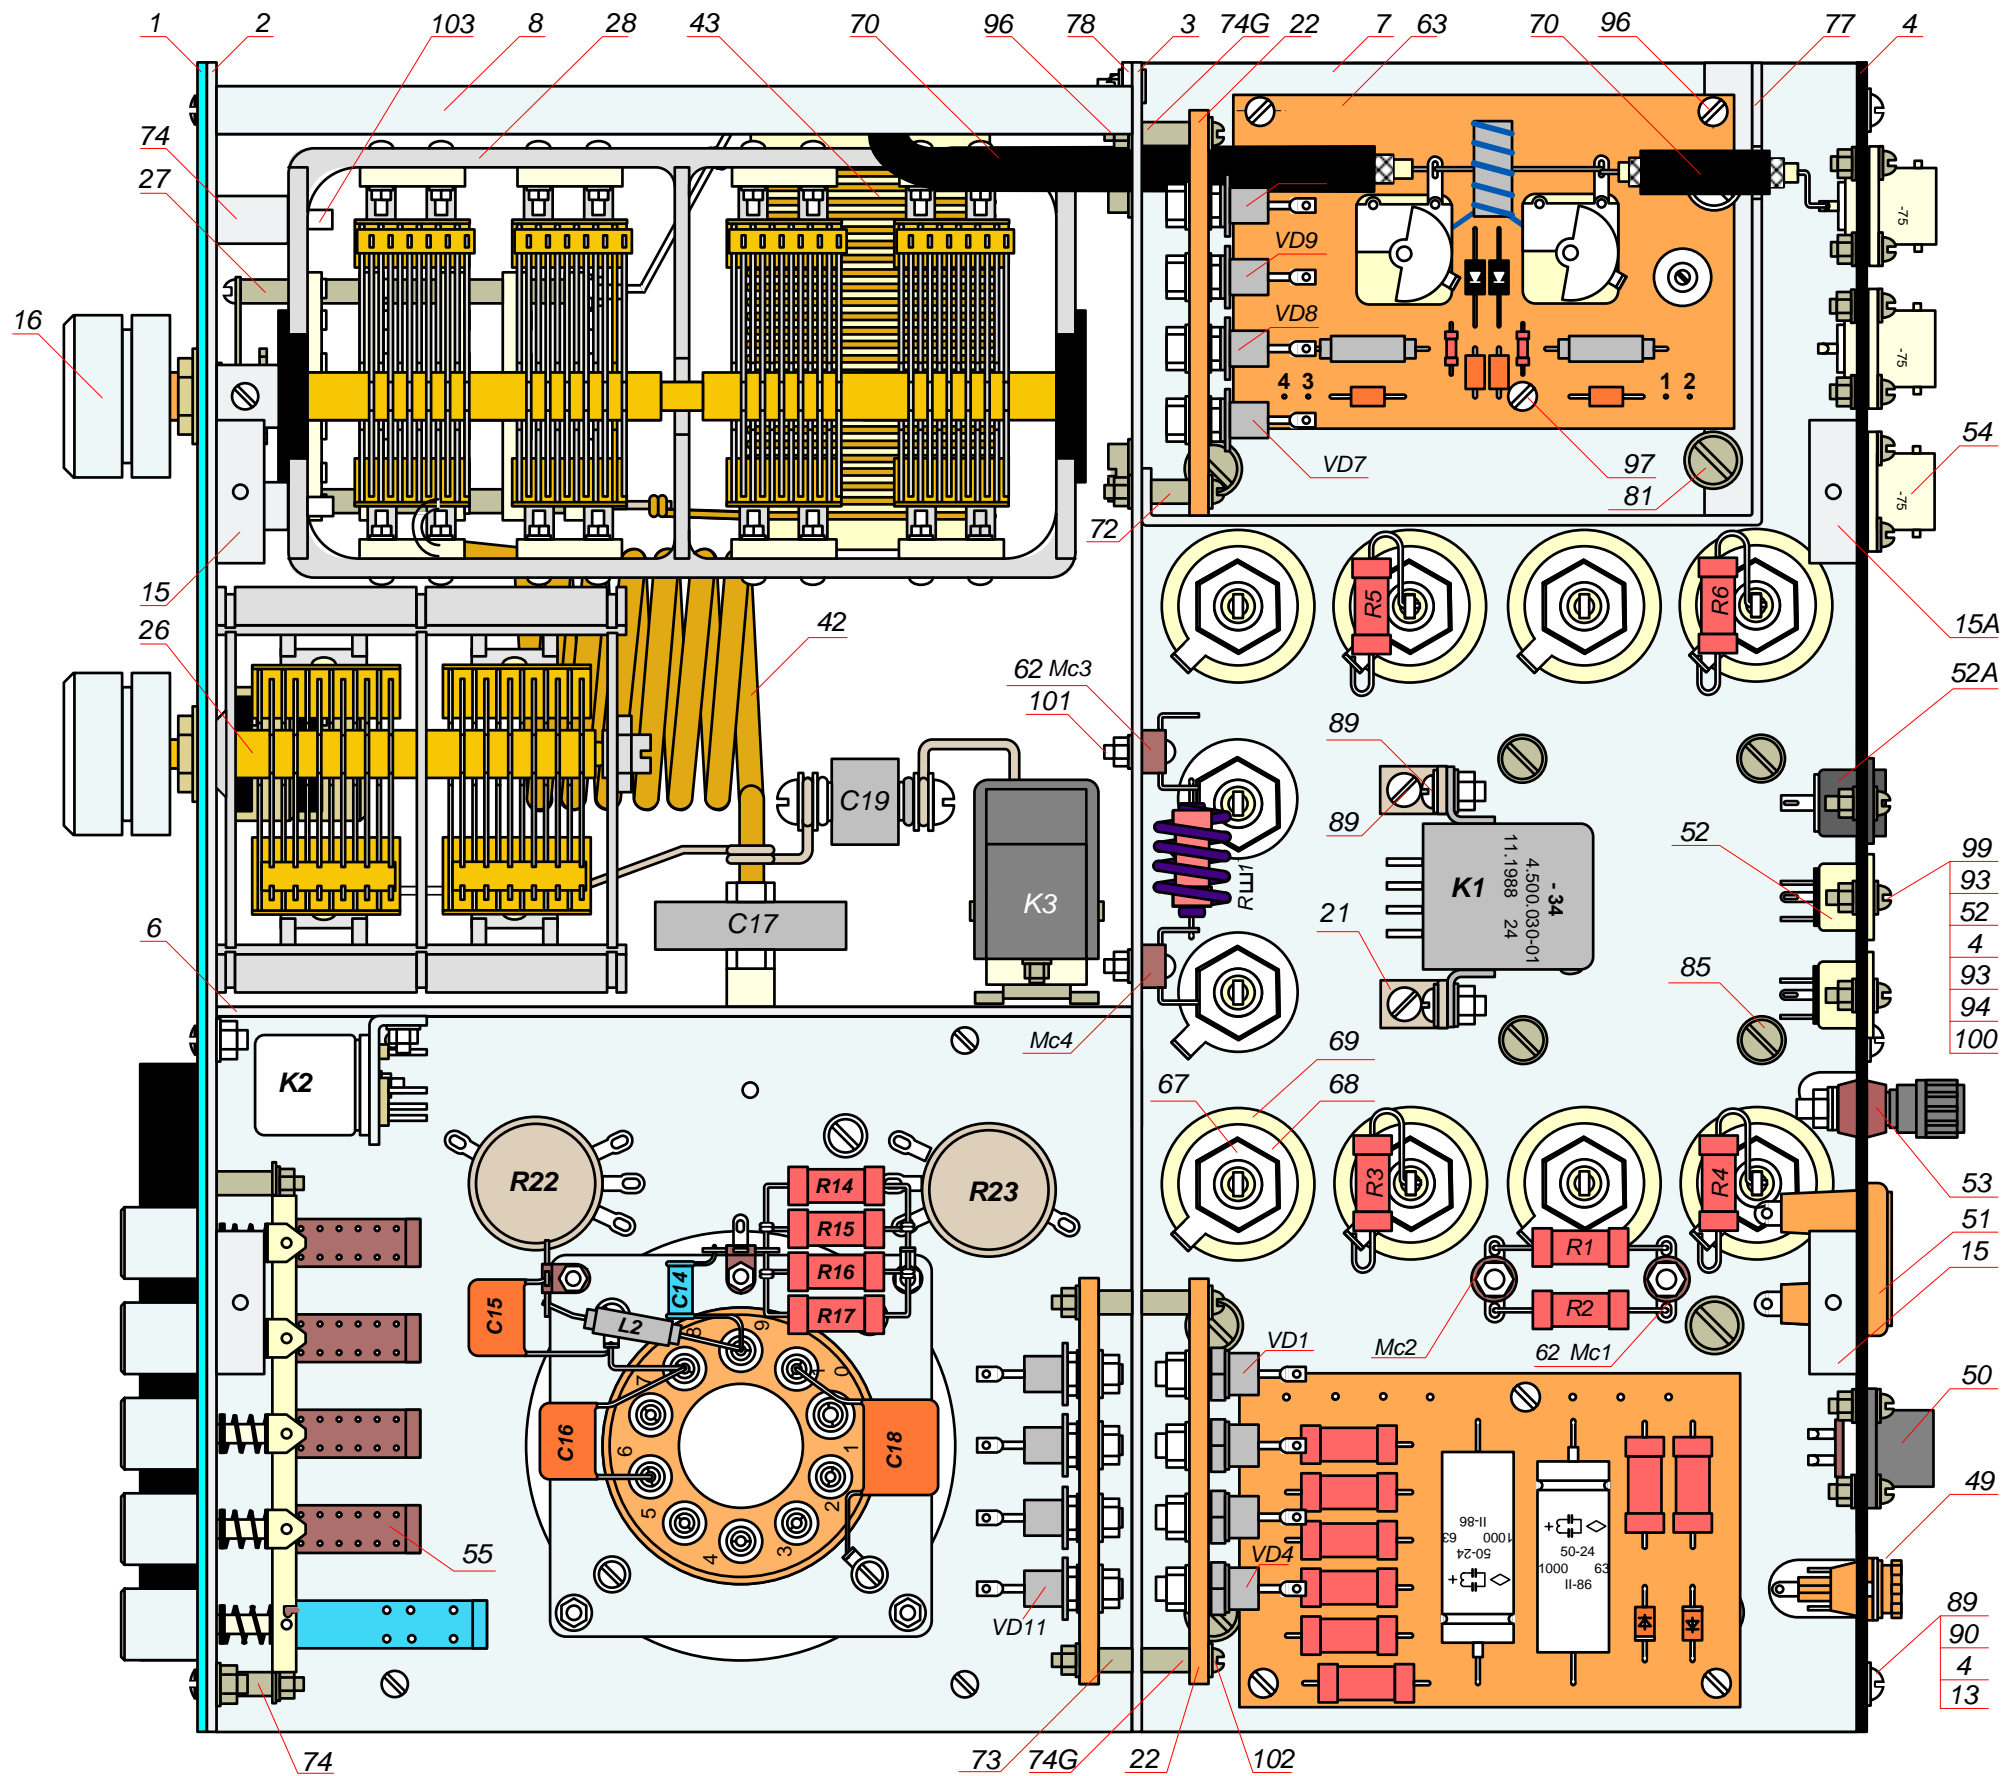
А. Сборочный чертёж усилителя DVA-300А. Вид сверху со снятыми верхней и нижней крышками.
